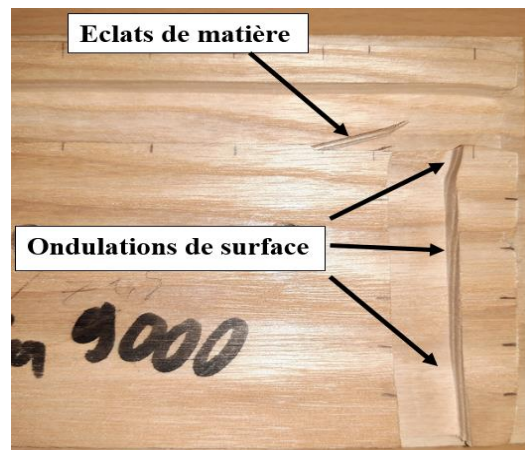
Etat de surface en usinage robotisé à 9000 mm/min du Hêtre
